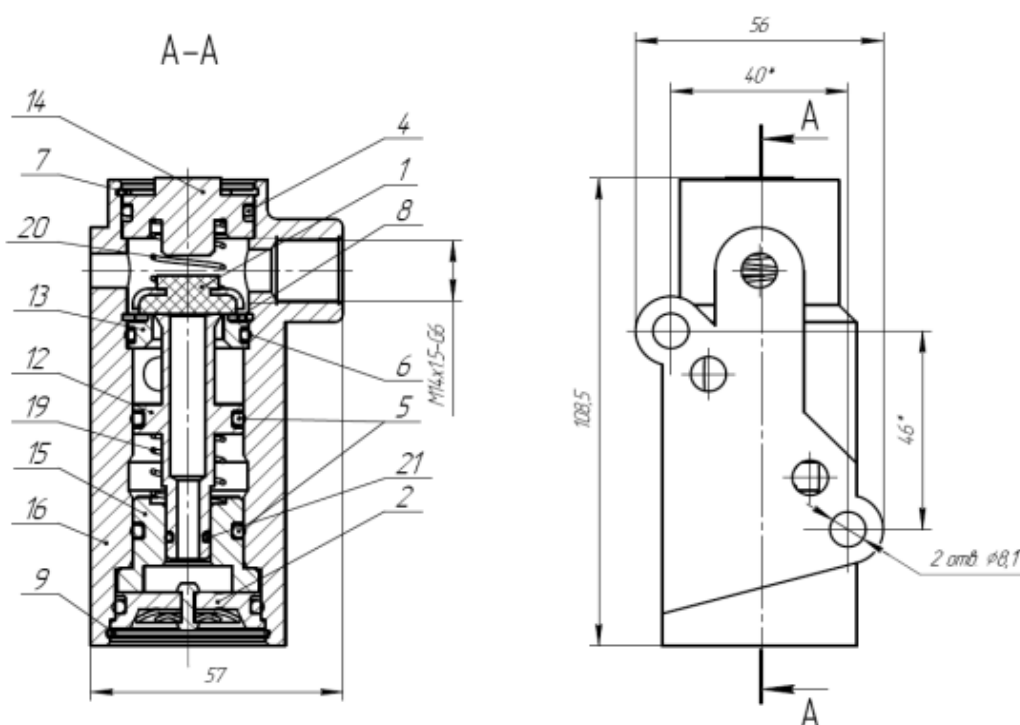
Конструкція макетного зразка прискорювального клапана
